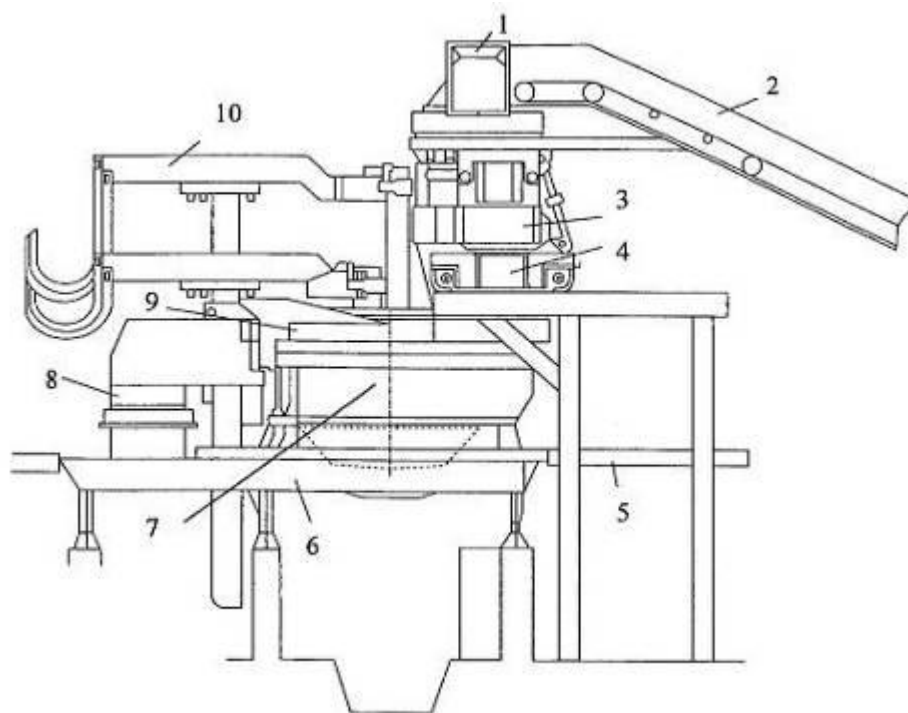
Схема установки нового оборудования на электродуговой печи: 1 – вытяжной колпак; 2 – ленточный конвейер для металлического лома; 3 – шахта; 4 – подъемное/приводное устройство; 5 – площадка; 6 – рама печи; 7 – кожух печи; 8 – портал; 9 – свод печи; 10 – электрододержатели
